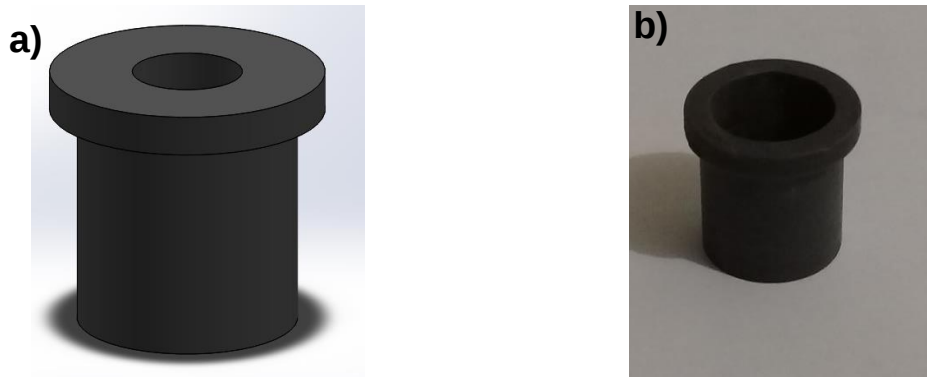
a) Diseño final de soporte roscado, b) soporte terminado.
